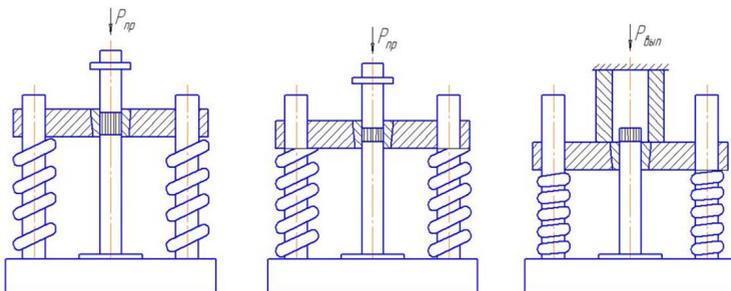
Схема двустороннего прессования порошков и выпрессовки изделия
